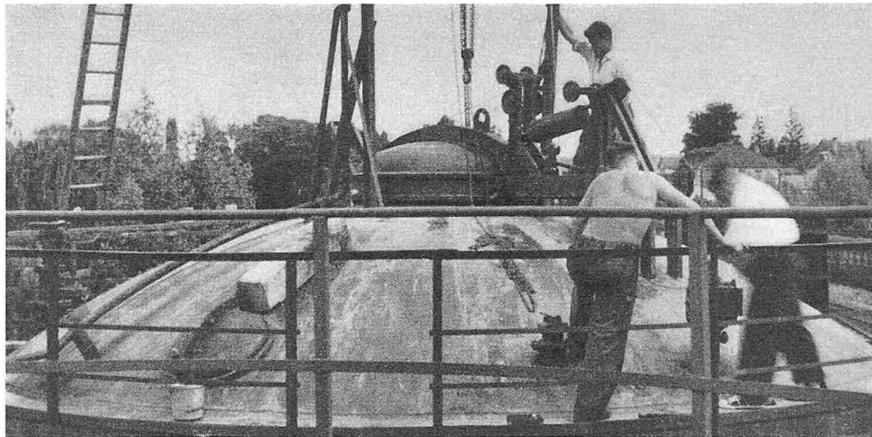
Prüfung der Bodenschweissnähte mit der Vakuump-Haube
